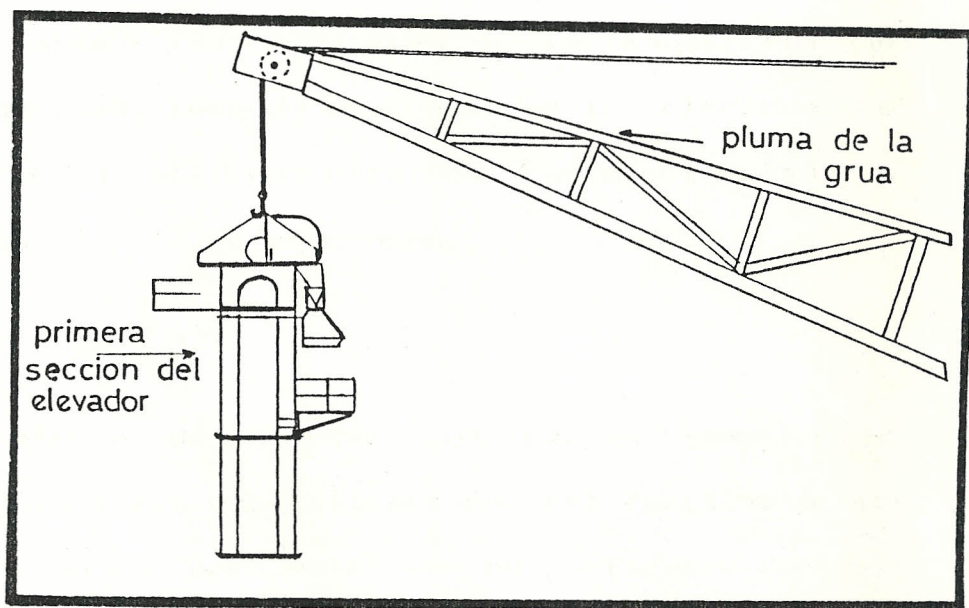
ESQUEMA DE ARMADO DE LAS DOS PRIMERAS SECCIONES DEL ELEVADOR DE CANGILONES.
